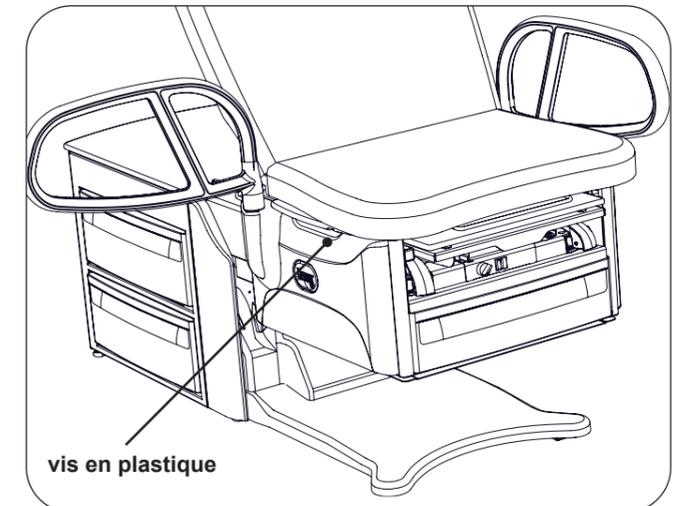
Emplacement de la vis d'arrêt en plastique blanc
